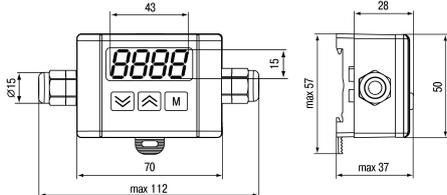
Габаритные размеры корпуса НЗ
